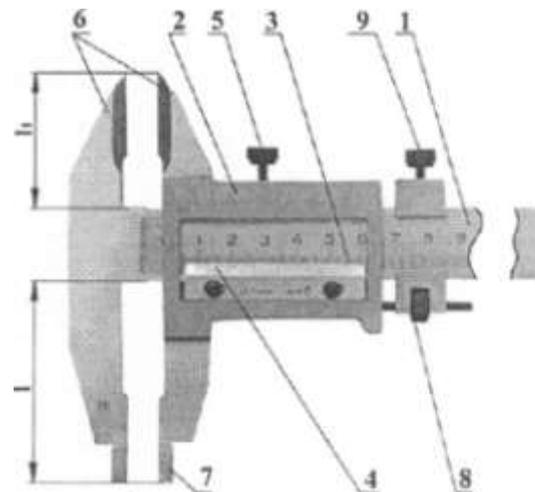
Устройство штангенциркуля ШЦ-П-250-0,1-2:
